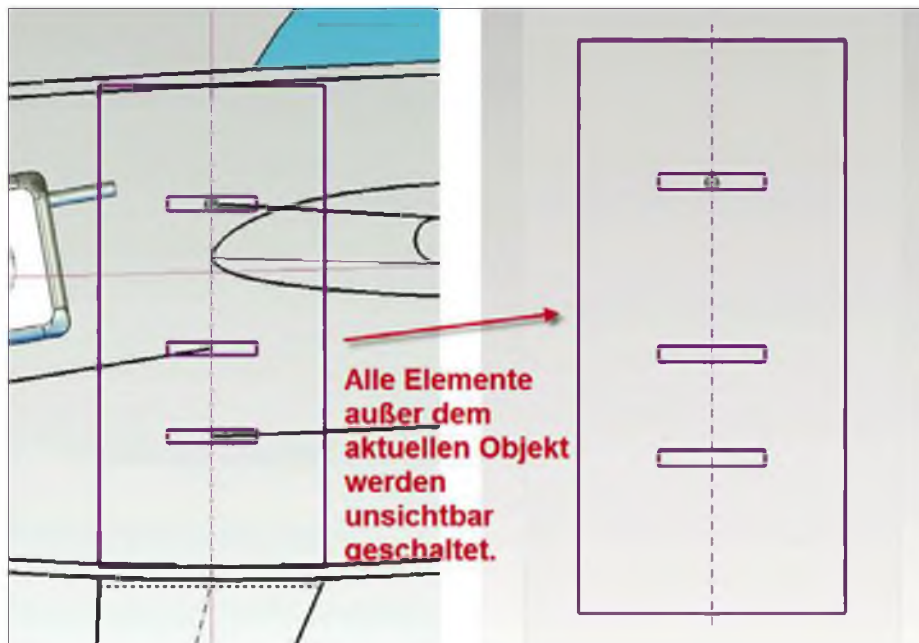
Isoliert dargestellter Spant mit Verzapfungen für Einbauten.
